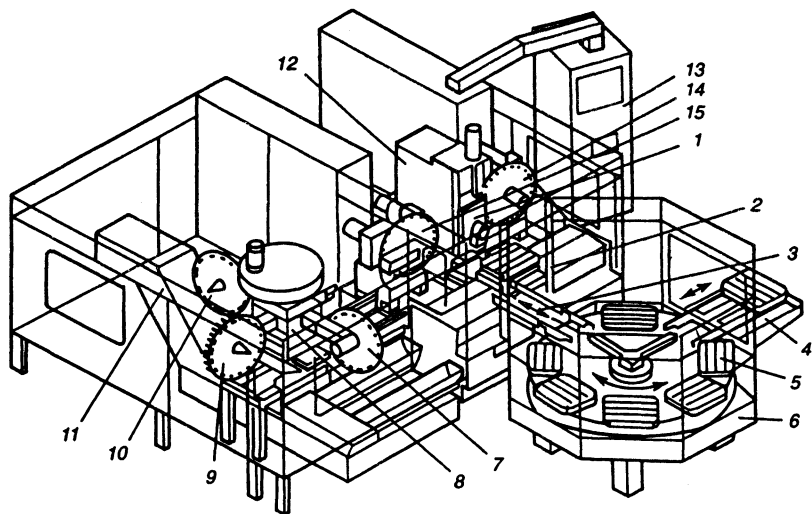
ГПМ горизонтальной компоновки для обработки заготовок корпусов
